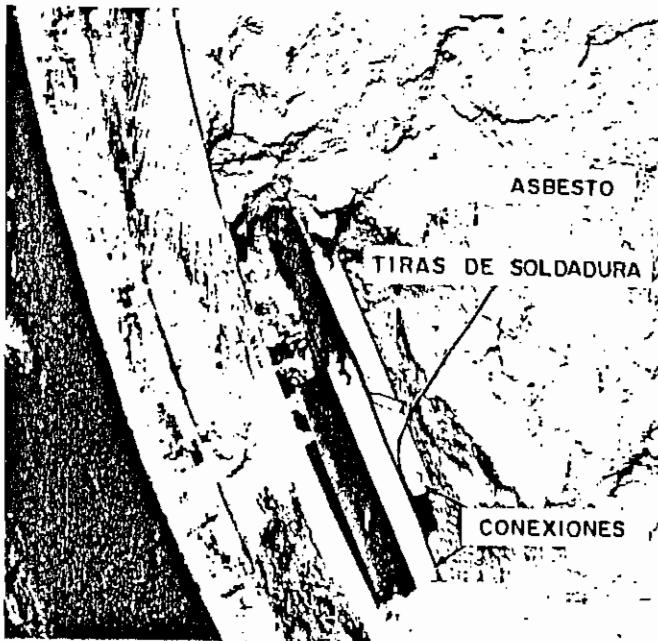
Conexión de la bobina del campo de excitación, tira de soldadura insertada y area adyacente cubierta con asbesto
